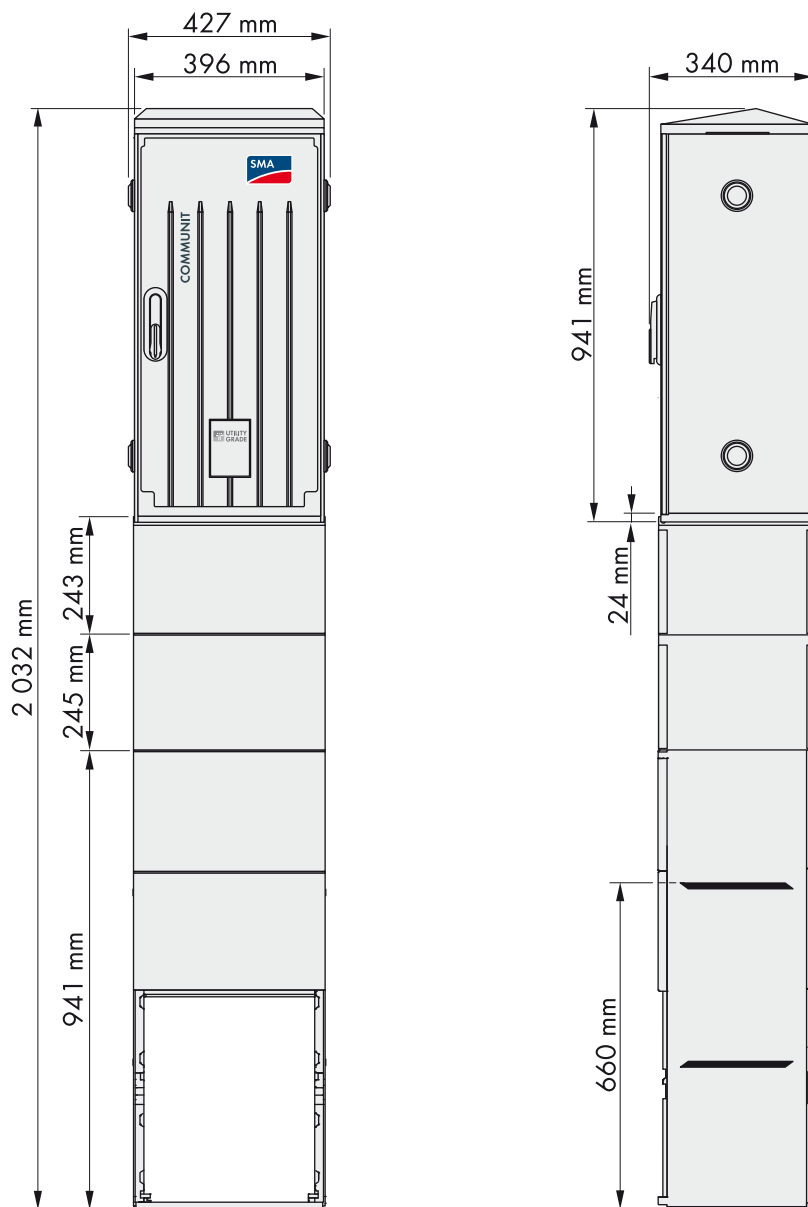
Dimensioni di Communit per il montaggio su zoccolo
